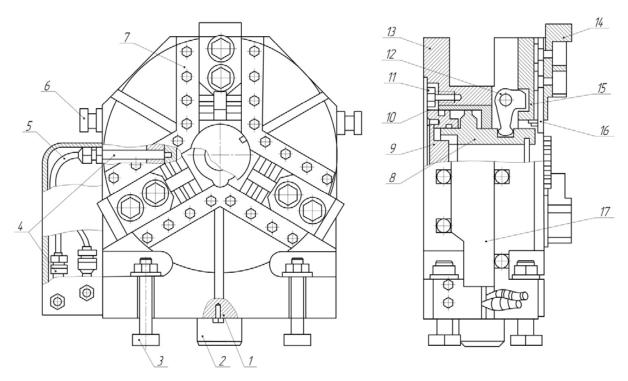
Стол круглый горизонтально-вертикальный, неподвижный: 1 — шпонка; 2, 6 — штыри; 3 — болт; 4 — штуцер; 5 — трубка; 7 — планка; 8 — поршень; 9 — упор; 10 — цилиндр; 11 — крышка; 12 — рычаг; 13 — корпус; 14 — кулачок; 15 — ползун; 16 — уголок; 17 — кожух
